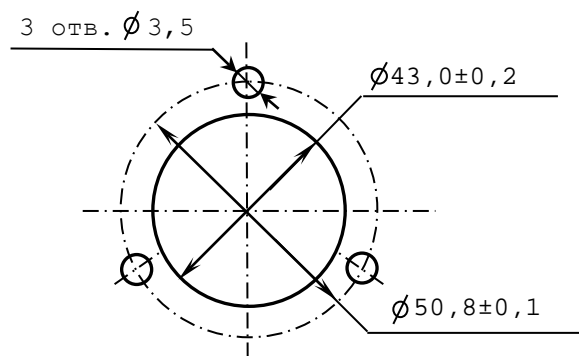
Установочные размеры штурвала серии WSB
